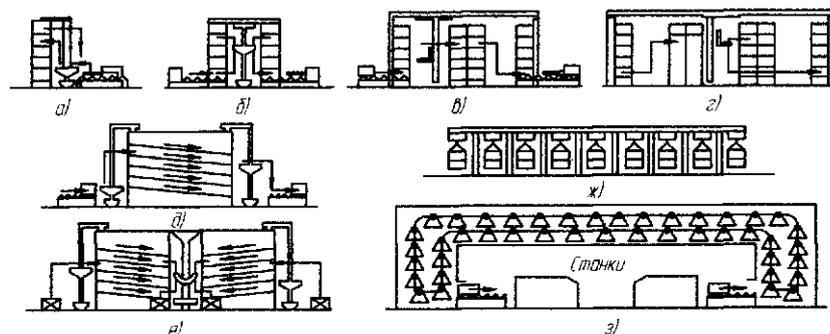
Варианты механизированных и автоматизированных складов: а, б – со стеллажными кранами-штабелёрами; в, г – с мостовыми кранами-штабелёрами; д, е – с гравитационными стеллажами; ж – подвесной на базе подвесного толкающего конвейера; з – элеваторный
